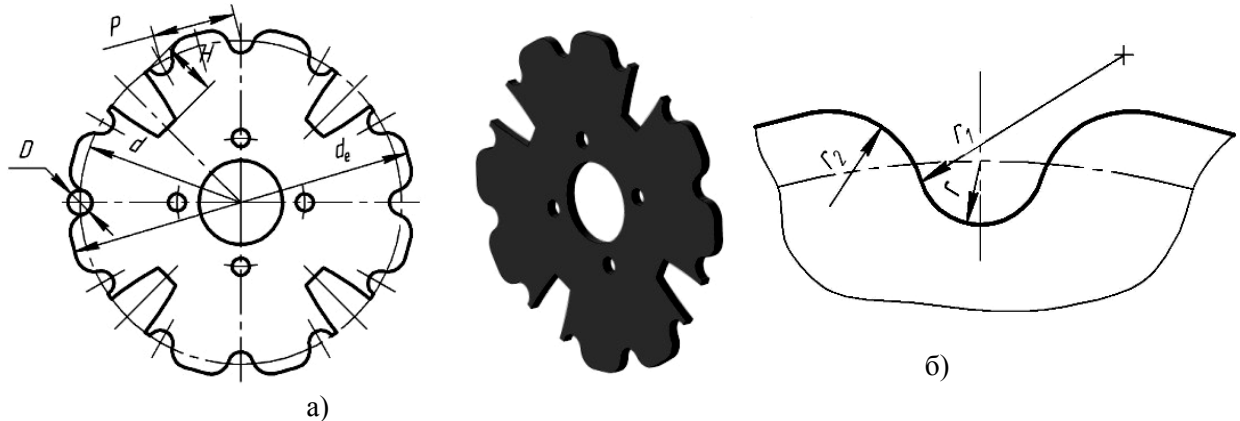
Конструкція спеціальної приводної зірочки: а) зірочка; б) конструктивні параметри впадини
